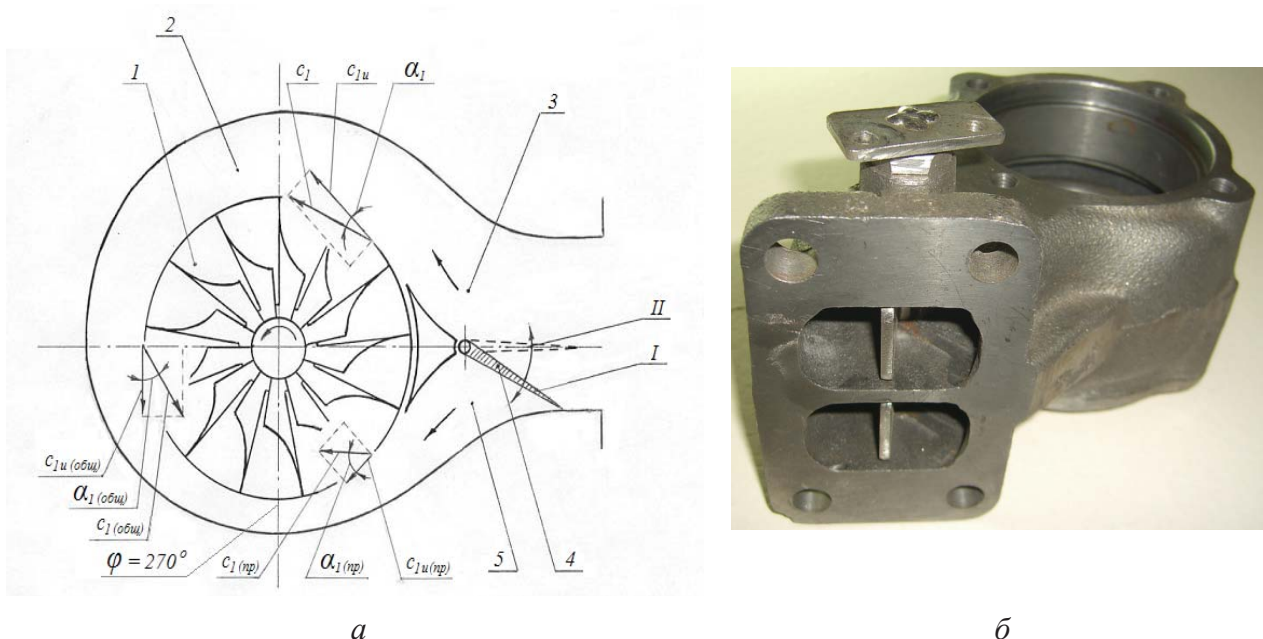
Схема способа регулирования (а) и корпус турбины (б)
